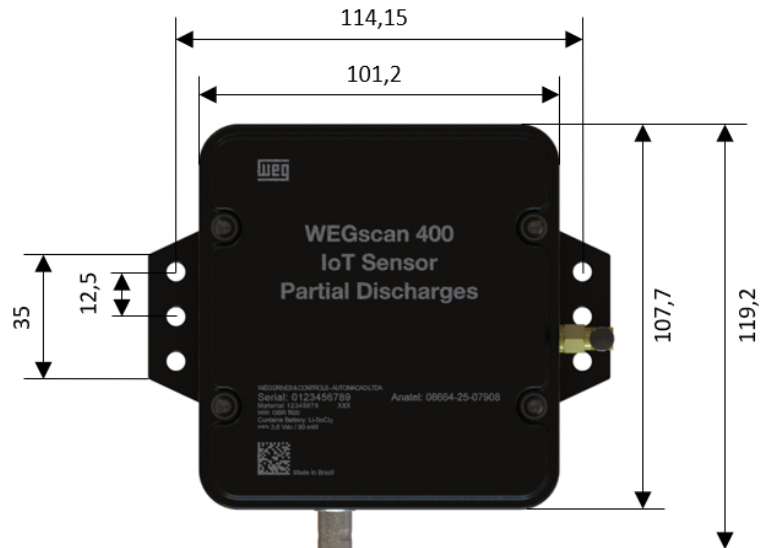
Dimensões [mm] externas do WEGscan400 com presilha para superfícies planas - Vista superior
